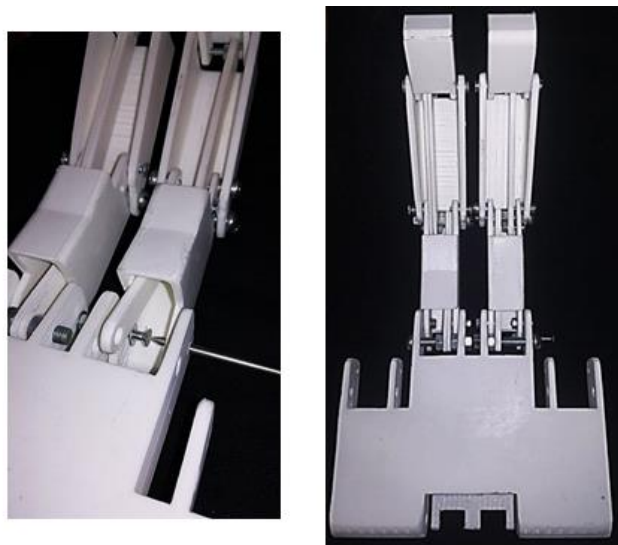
Proceso de montaje de los dedos mediante las piezas fabricadas en la impresora 3D
